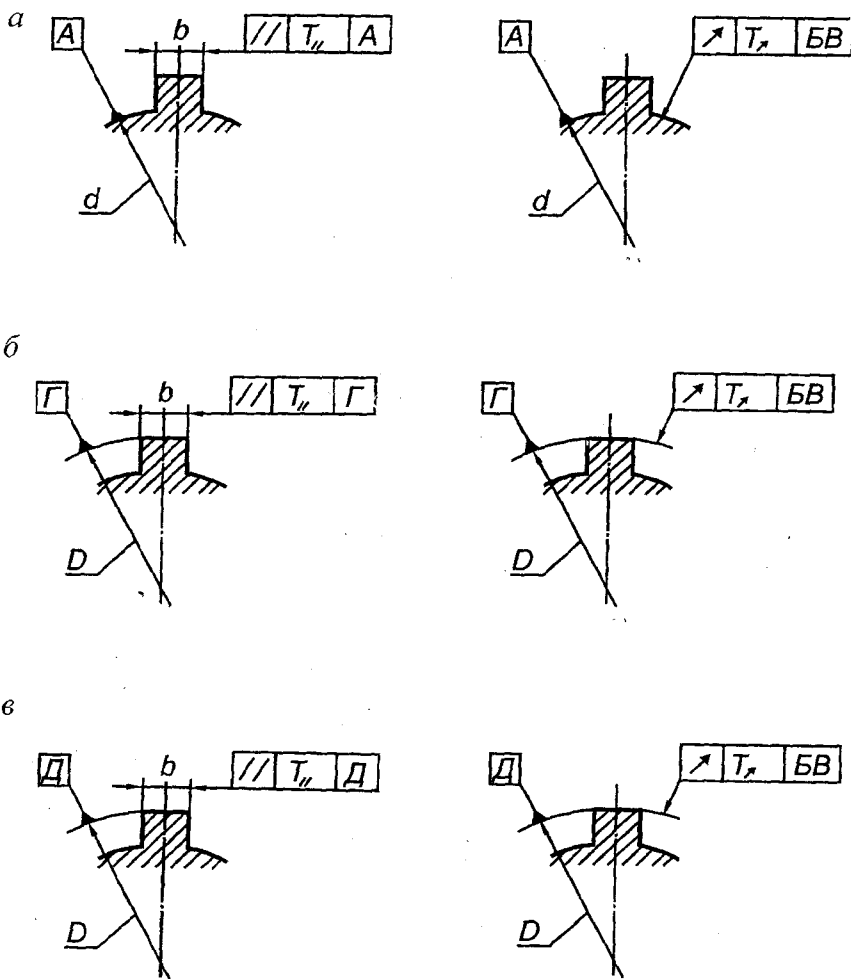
Обозначения допусков параллельности и радиального биения элементов наружной шлицевой поверхности:
